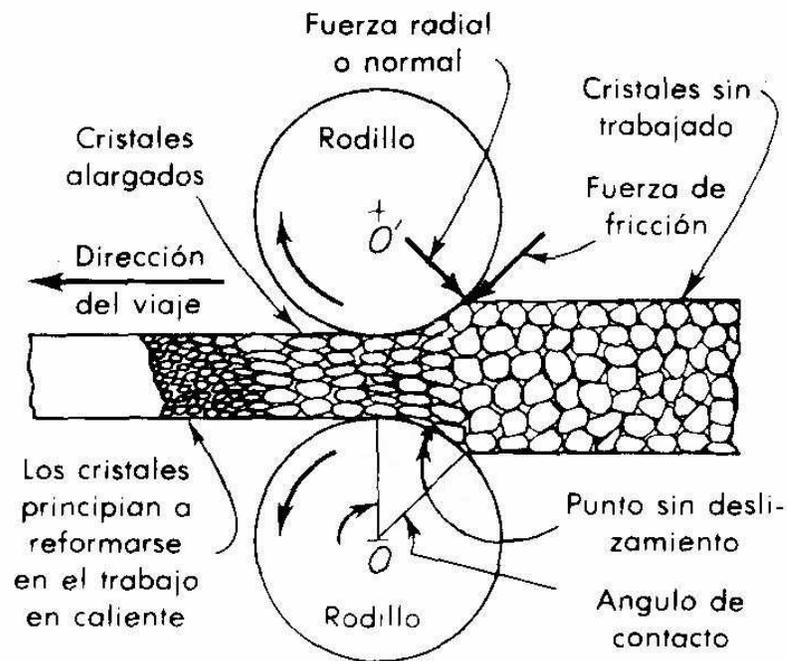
Proceso de laminación, específicamente laminado plano.
